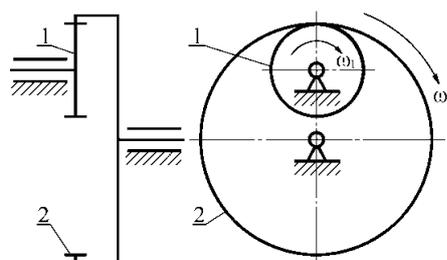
Зубчатая цилиндрическая передача внутреннего зацепления
